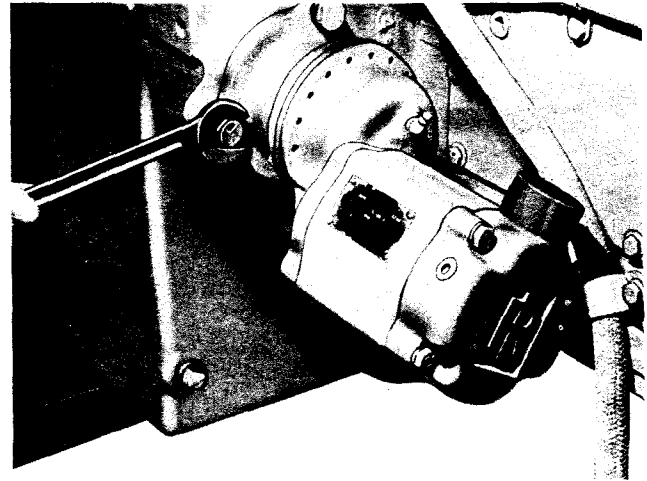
, (N10004). Remoción del motor de arranque de aire.
